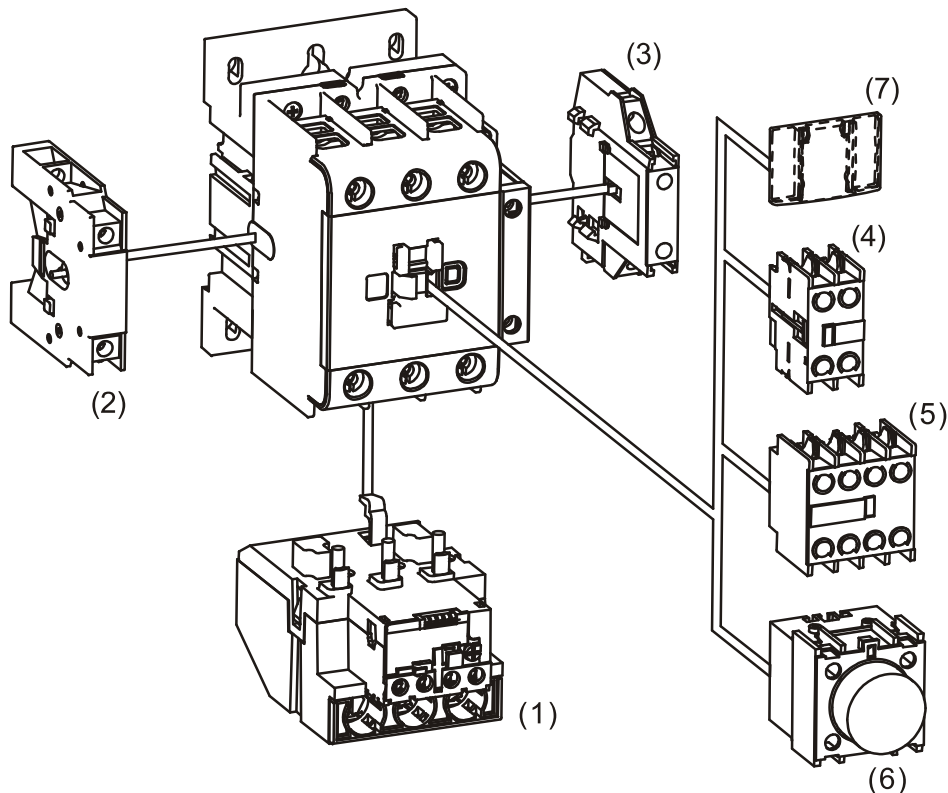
Контактор КМ-102 и схематичная установка аксессуаров
